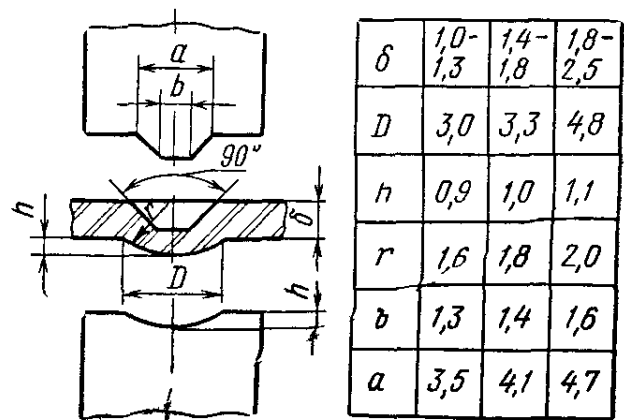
Рельеф Международного института сварки с размерами инструмента для полос толщиной δ
